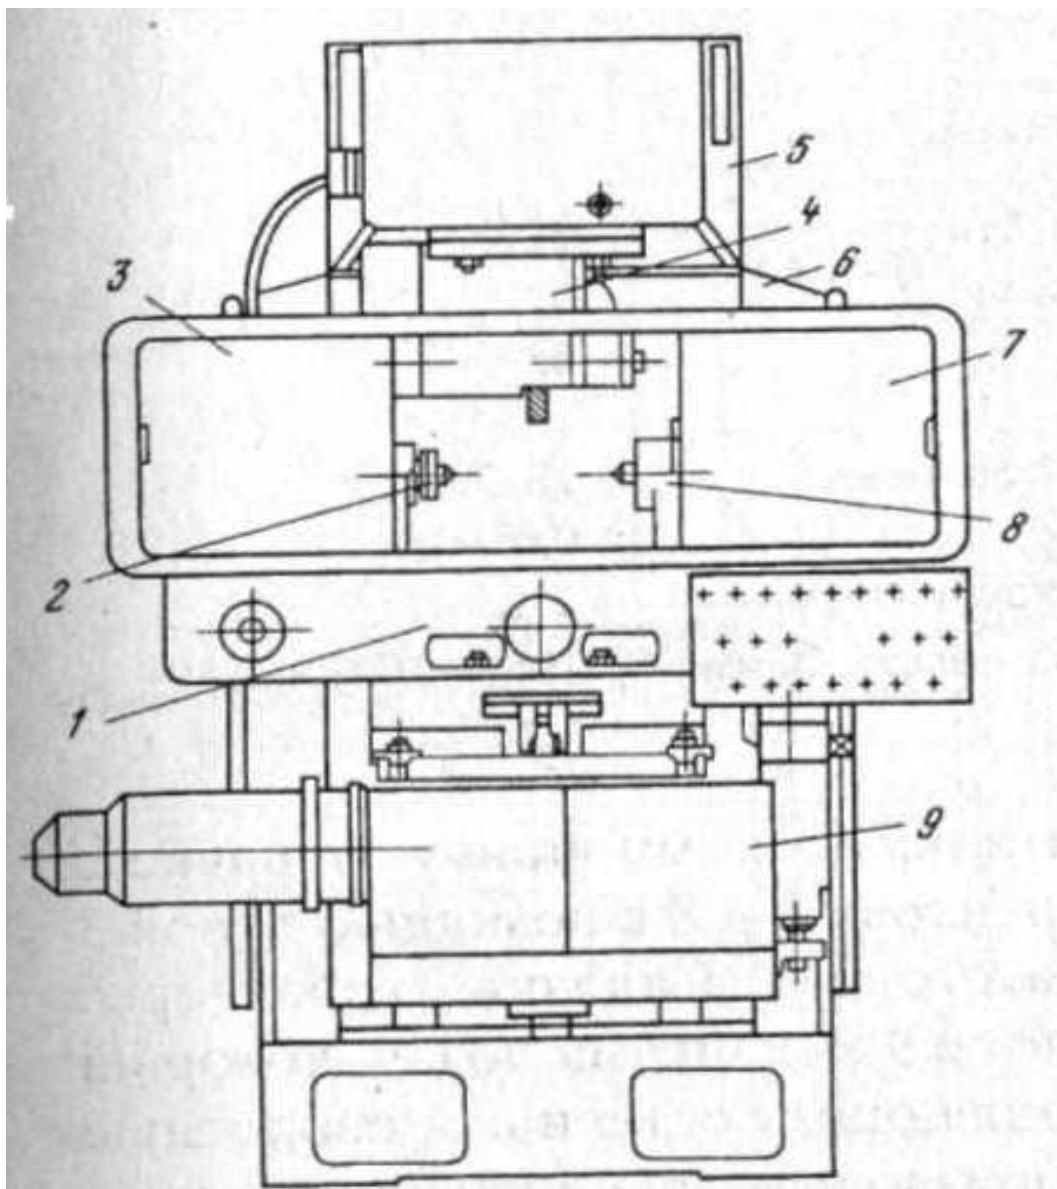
Общий вид зубошевинговального станка модели 5Б702В.
